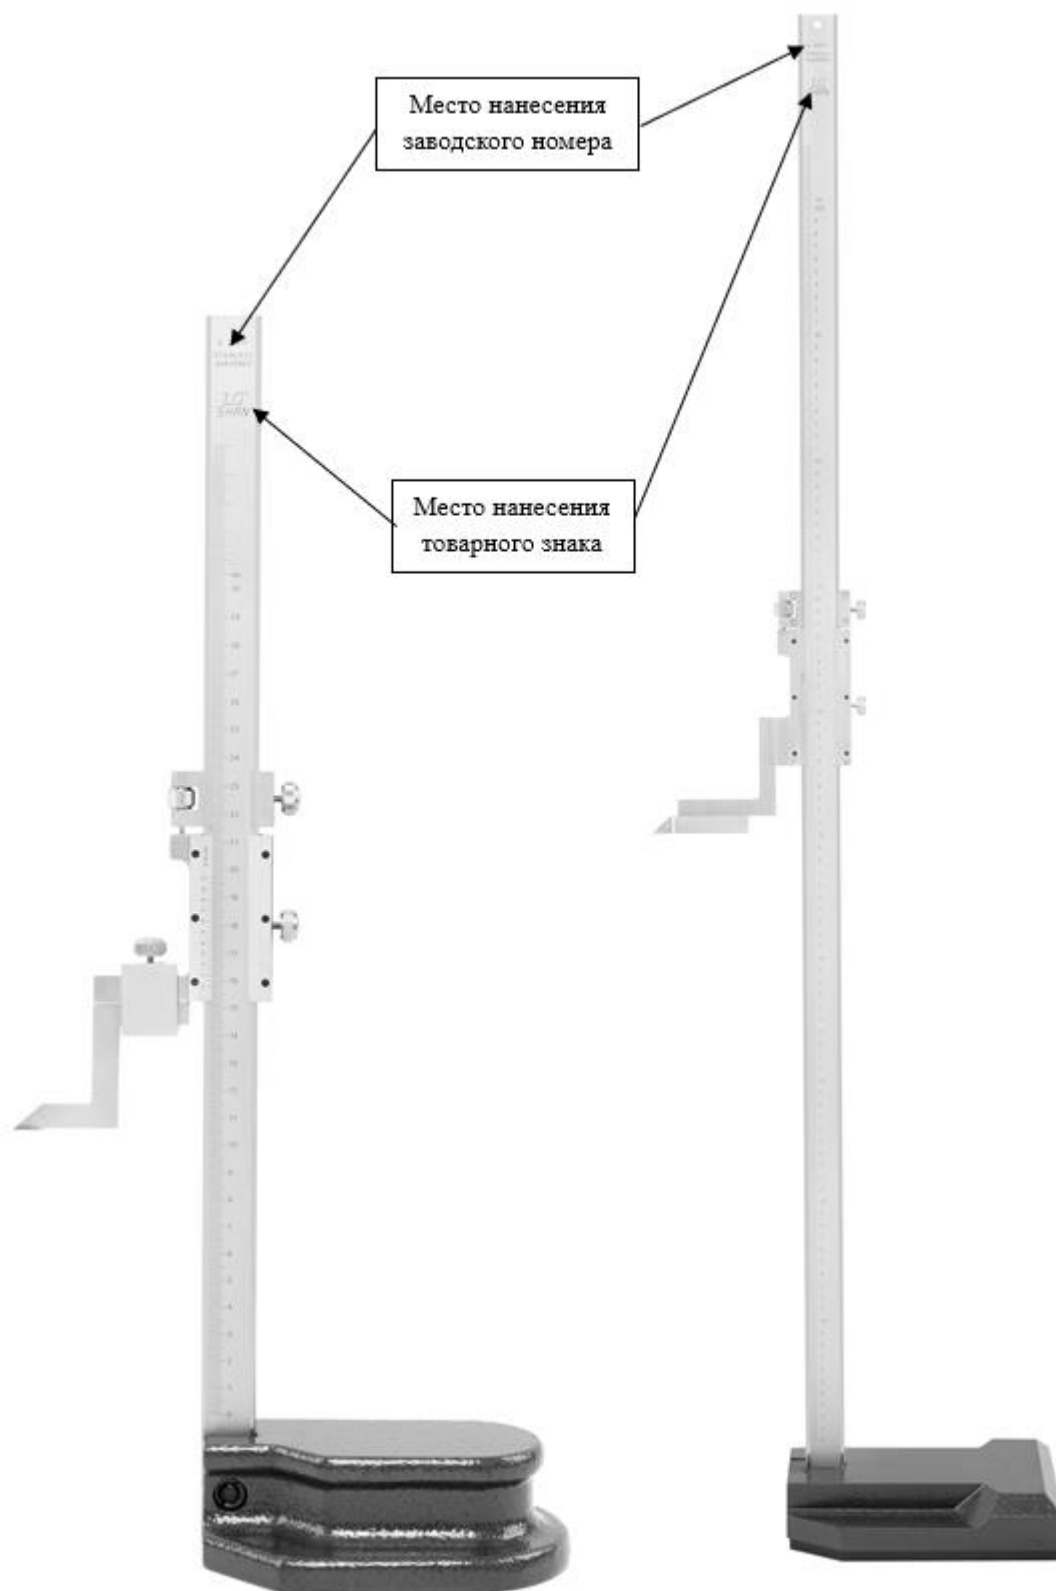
Общий вид штангенрейсмасов модели ШР, место нанесения заводского номера и товарного знака
